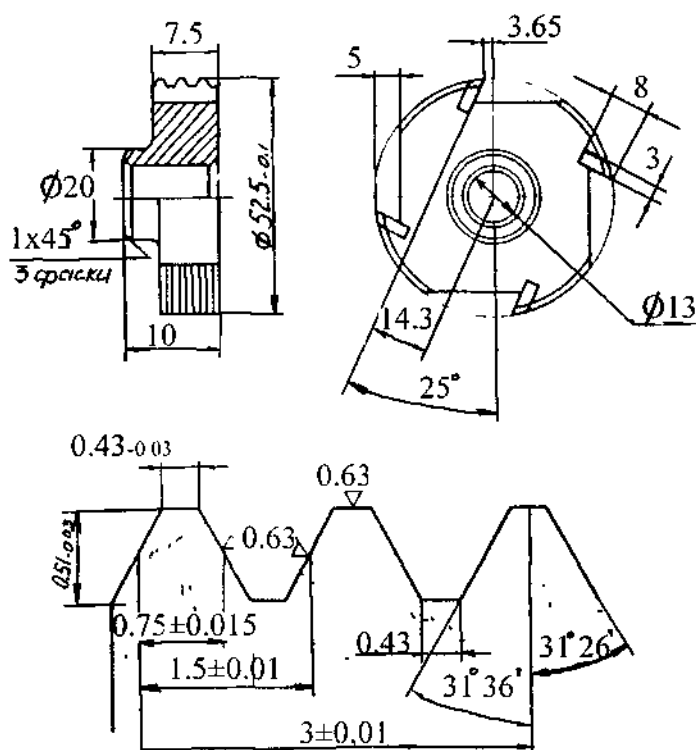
Гребенка с твердосплавными пластинами для нарезания окулярной резьбы.
